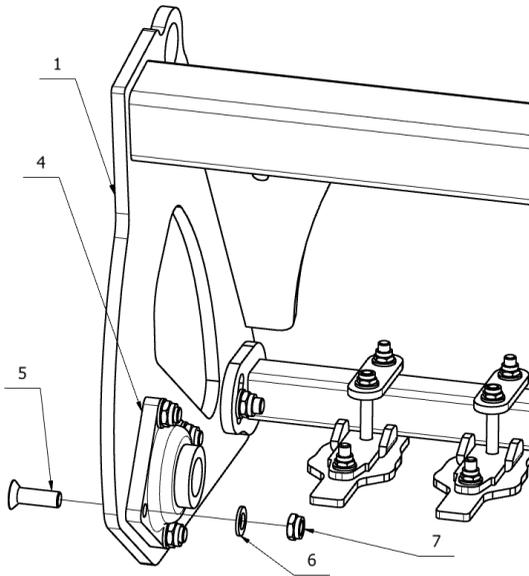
Scheibenwalze Ø600mm - Lagermontage.
